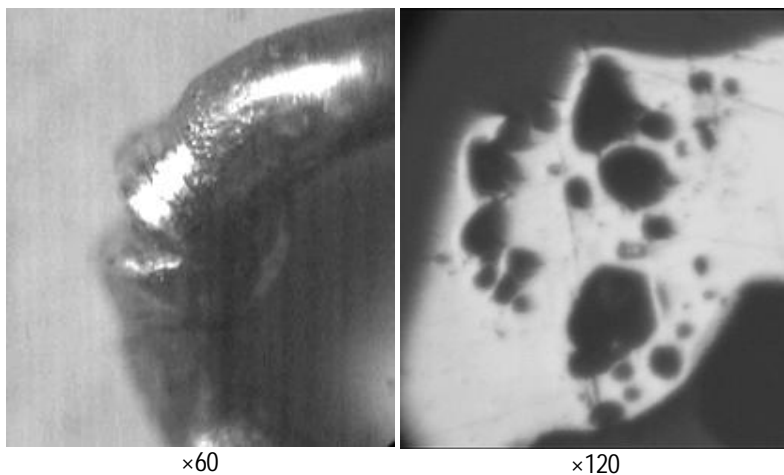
Внешний вид сварного соединения звена цепи сплава № 2
